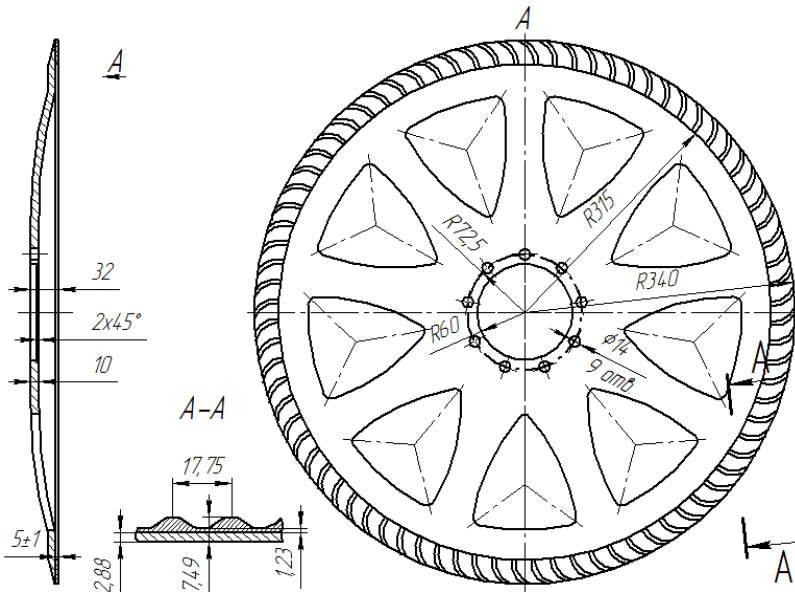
Схема конструкції диска копача із наплавленим шаром спіроїдної форми
